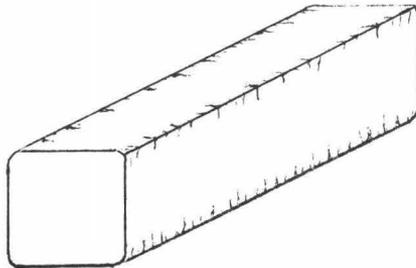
Grietas transversales en los vértices debidas a una palanquilla demasiado fría cuando se endereza.
